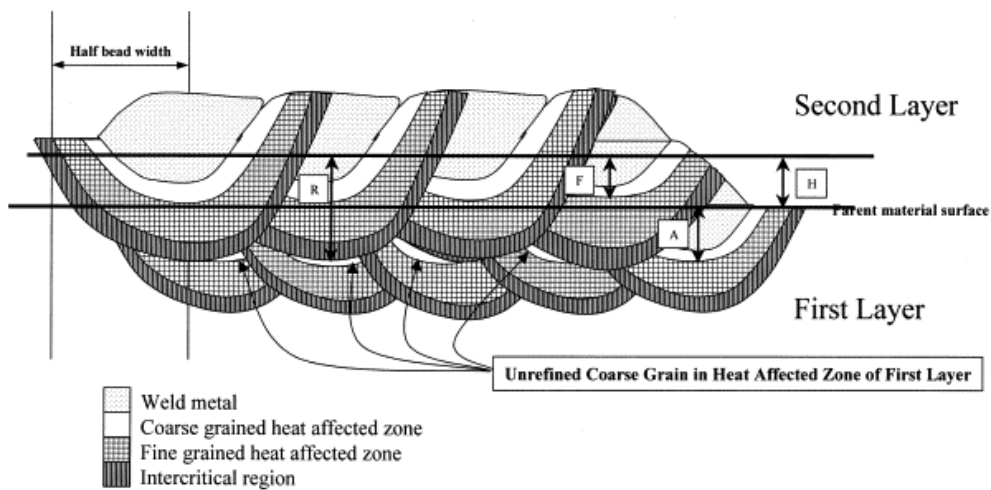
Temper bead weld 覆層銲接處理。
